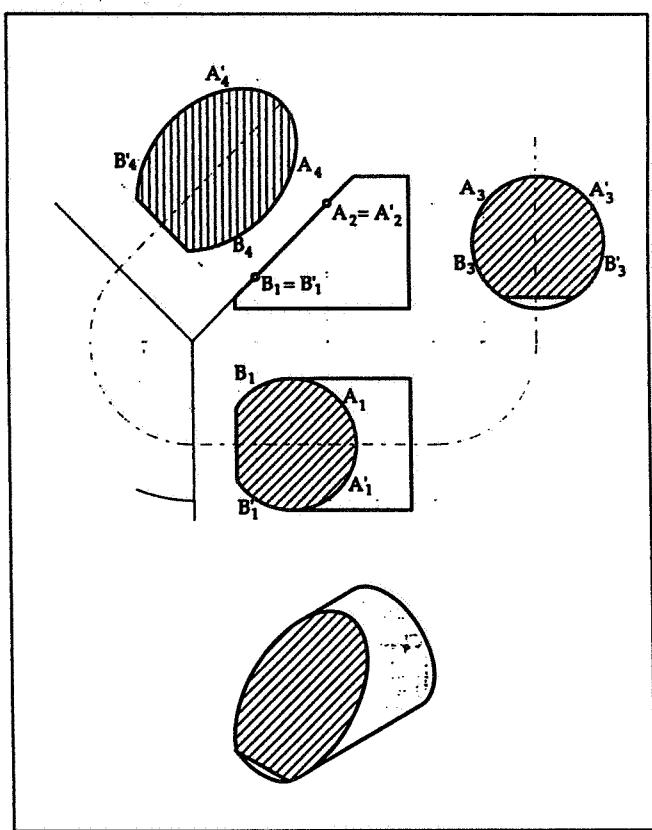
Sezione di un cilindro con un piano inclinato di 45° rispetto all'asse.
